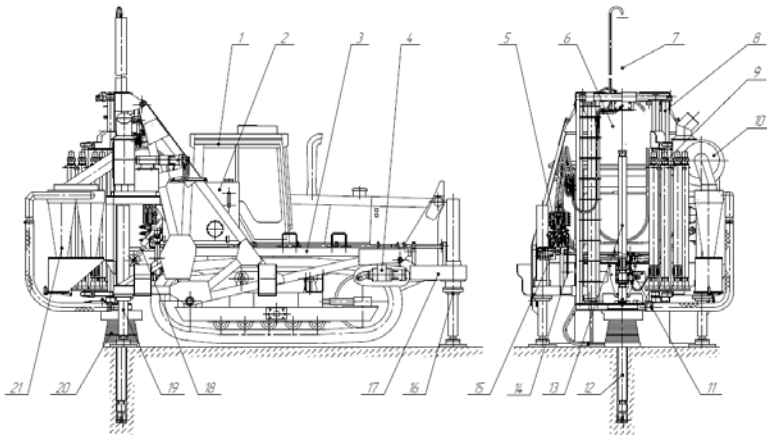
Буровой тракторный станок гидрофицированный БТС-150БГ в рабочем положении: 1-трактор Т10.1111-12; 2-гидравлический бак; 3-основная рама; 4-передняя насосная установка; 5-гидрооборудование; 6-вращатель; 7-гидроцилиндр подачи; 8-буровая рама; 9-механизм подачи штанг; 10-вентилятор; 11-основная насосная установка; 12-гладкая штанга; 13-противовибрационная штанга; 14-управление подачей топлива двигателя трактора; 15-пульта управления; 16-передний домкрат; 17-рама передних домкратов; 18-гидроцилиндр наклона; 19-задний домкрат; 20-пылеприемник; 21-циклон
